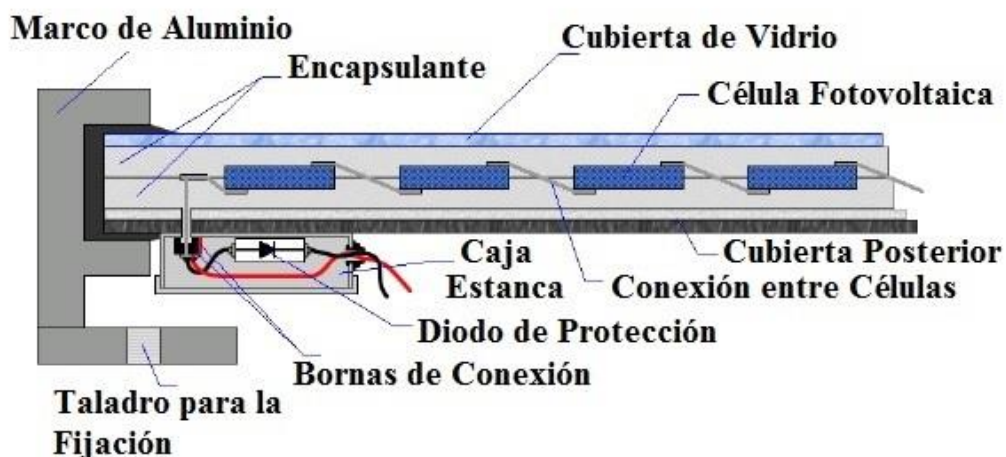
Elementos de un panel Fotovoltaico Fuente [ingemecanica.com](http://ingemecanica.com)
